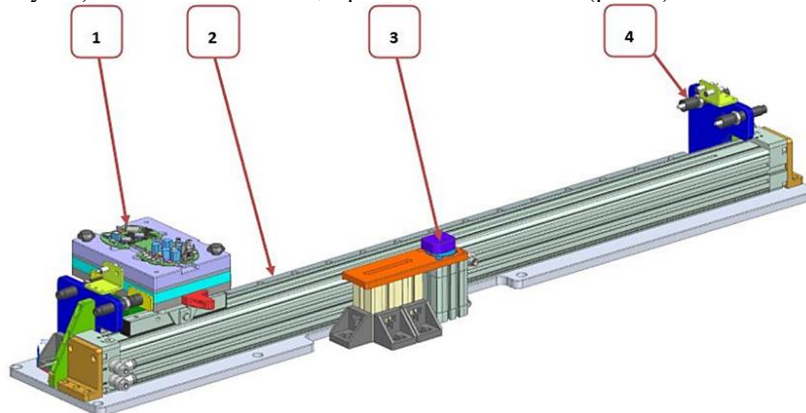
3D CAD-модель запропонованого горизонтального вузла маніпулятора: 1 - станина друкованої плати з її дисплеєм; 2 - лінійний горизонтальний привід по одній осі; 3 - упор станини; 4 - амортизатор
